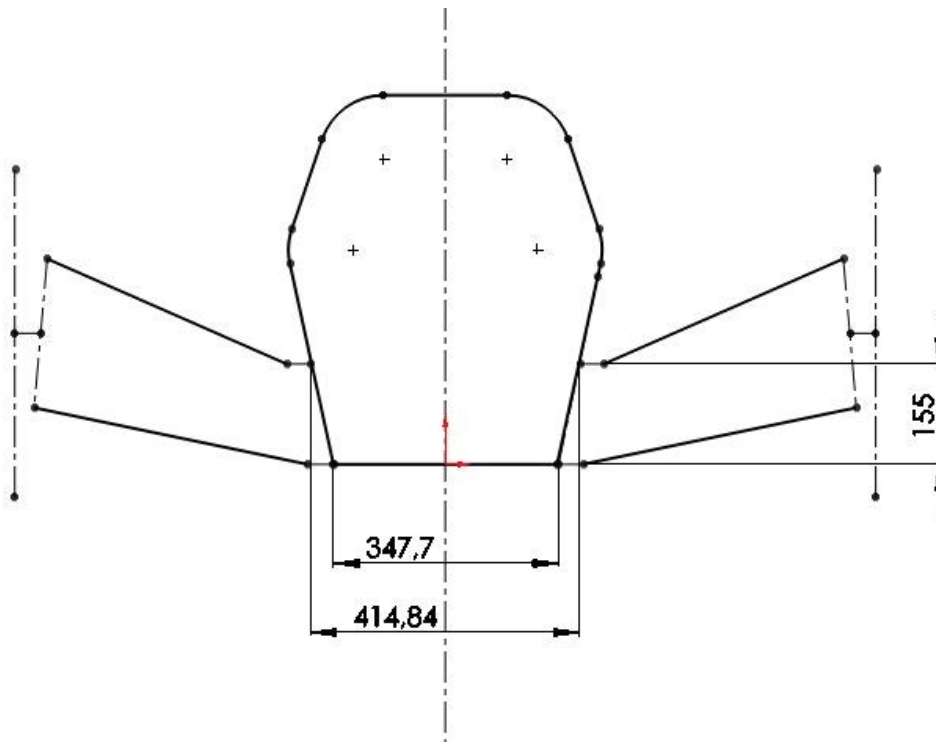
Vista da seção de aplicação do carregamento. (Arquivo próprio).
